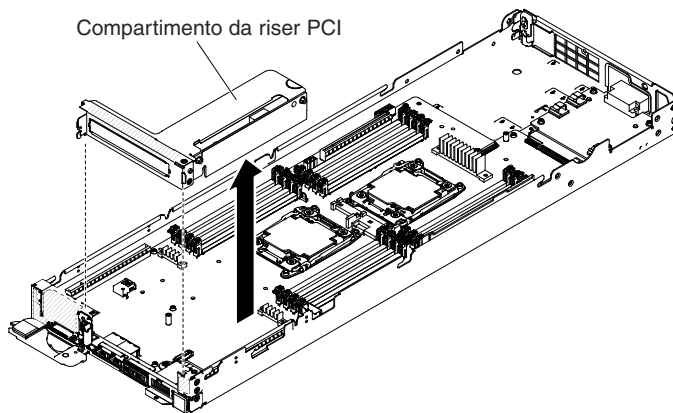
Remoção do conjunto de compartimento da placa riser PCI
